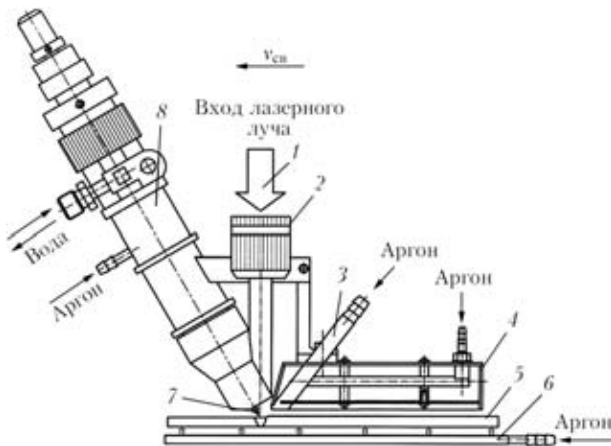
Схема гибридного лазерно-дугового процесса сварки: 1 — лазерный луч; 2 — устройство для фокусировки; 3 — приспособление для дополнительной подачи защитного газа; 4 — приспособление для защиты зоны сварки и остывающего металла шва и ЗТВ; 5 — свариваемый образец; 6 — приспособление для защиты обратной стороны соединения; 7 — вольфрамовый электрод; 8 — сварочная горелка для сварки ТИГ титана
